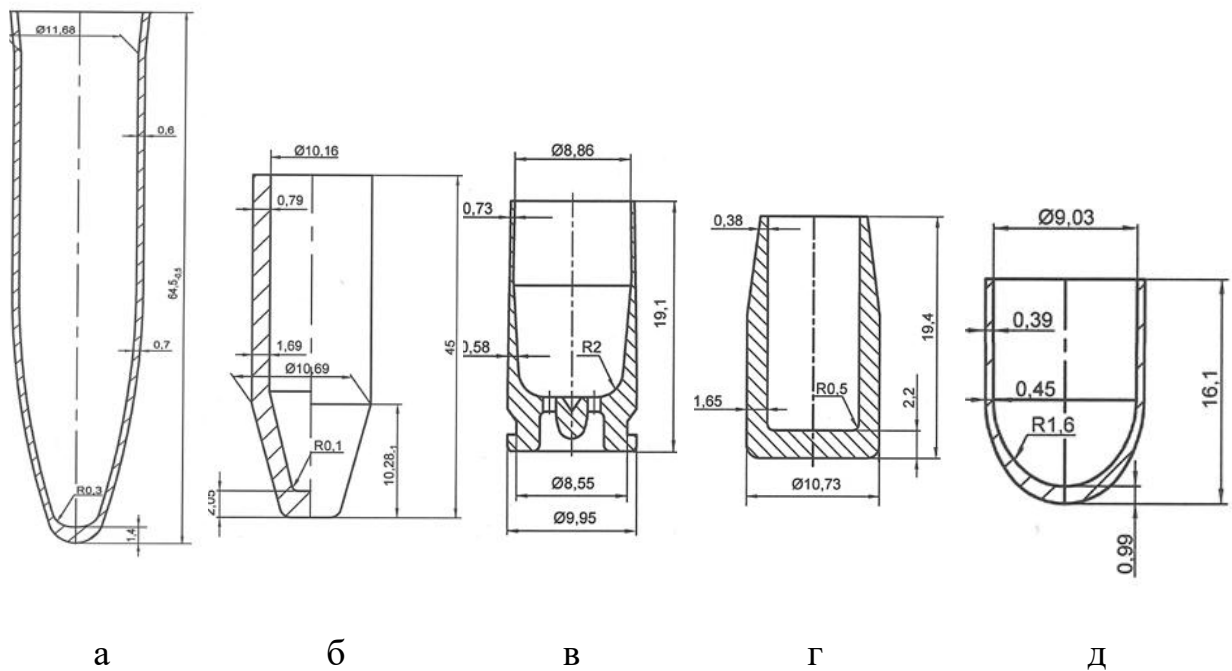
Металеві елементи патронів, що виготовляються за допомогою комбінованого витягування: а - оболонка; б - піростакан; в- пістолетна гільза; г - корпус трасера; д - оболонка до пістолетного патрону
